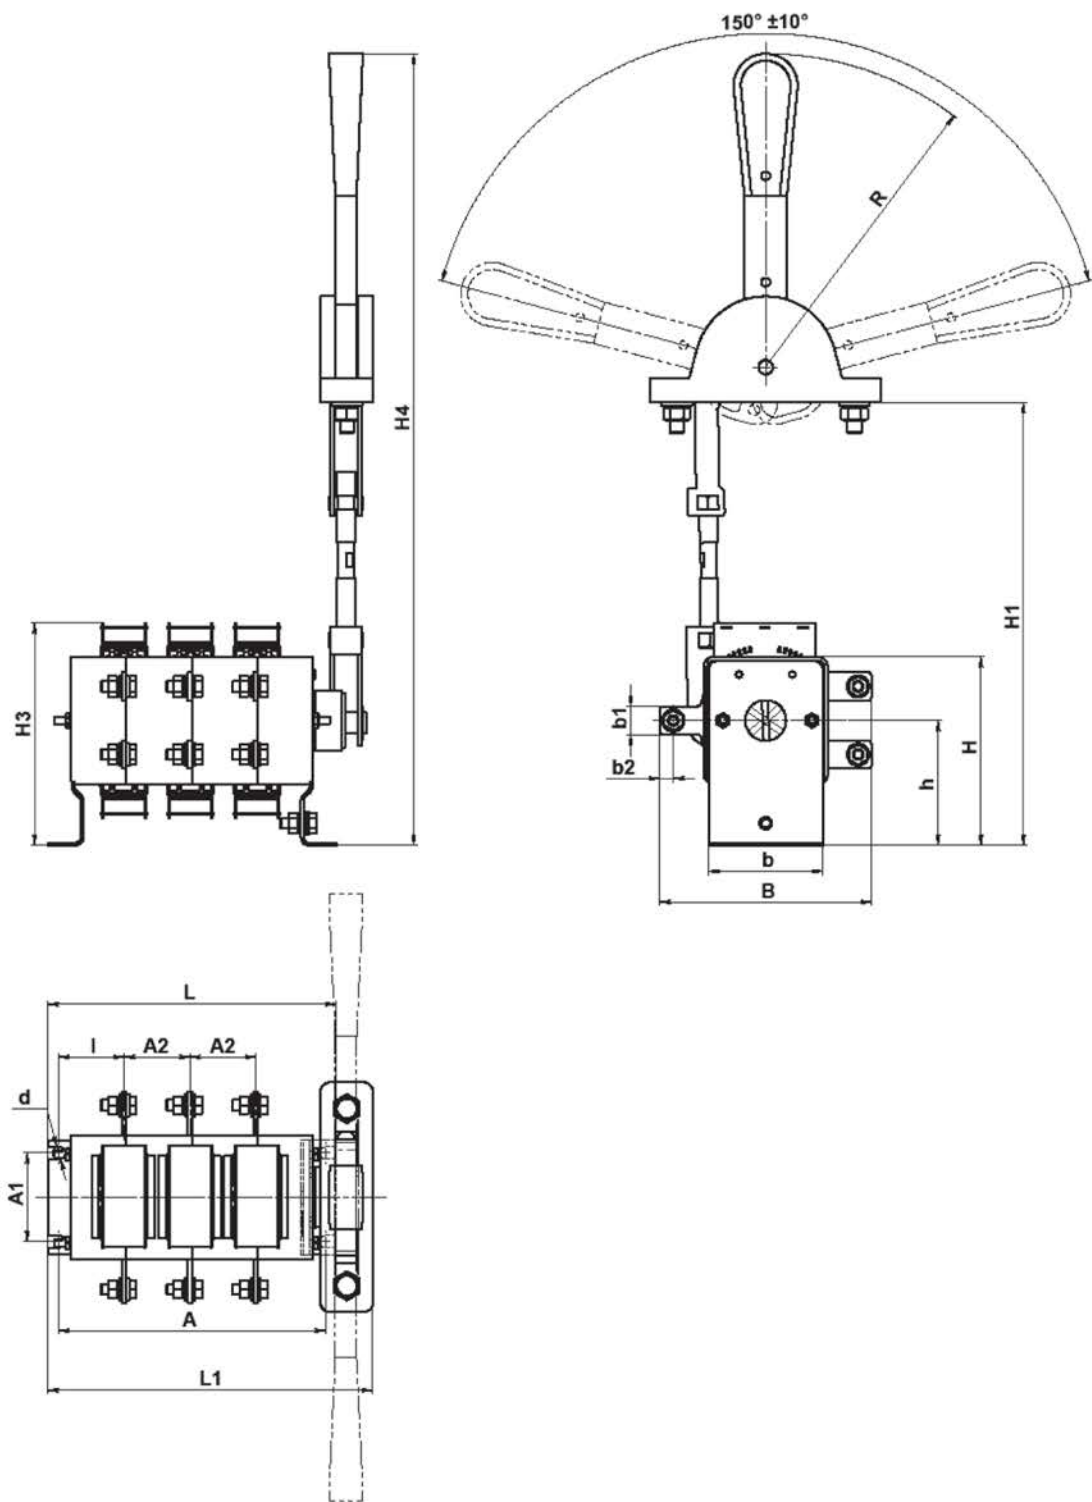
Выключатель-разъединитель трехполюсный на два направления с передней поворотной рукояткой.
